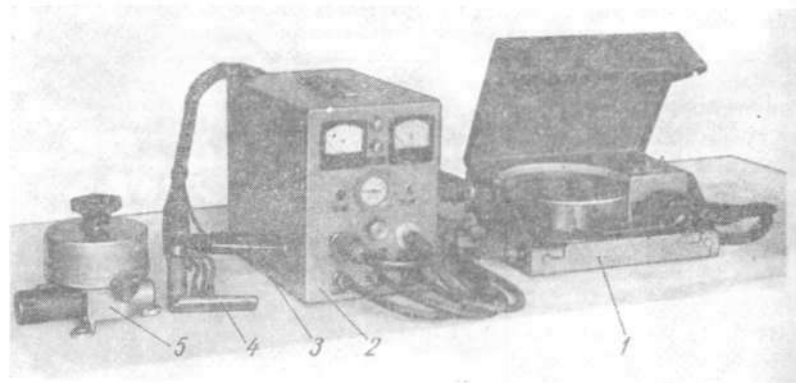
Полуавтомат ПГТ-3 для сварки плавящимся электродом в защитных газах.
